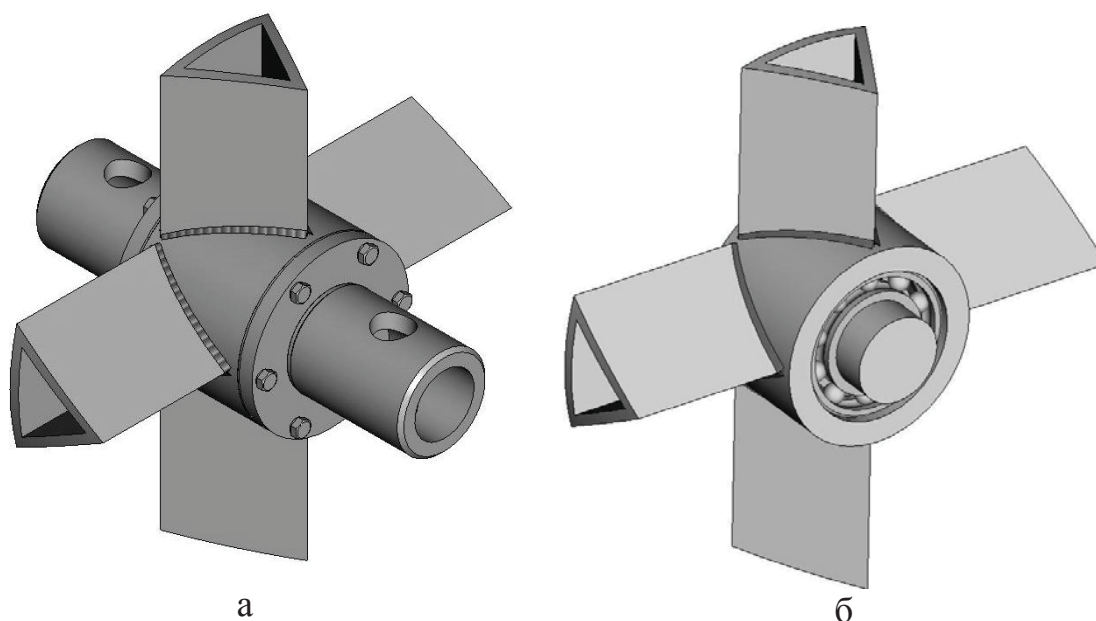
Конструкции опорных подшипниковых узлов с типовыми уплотняющими крышками (а) и без них (б)
